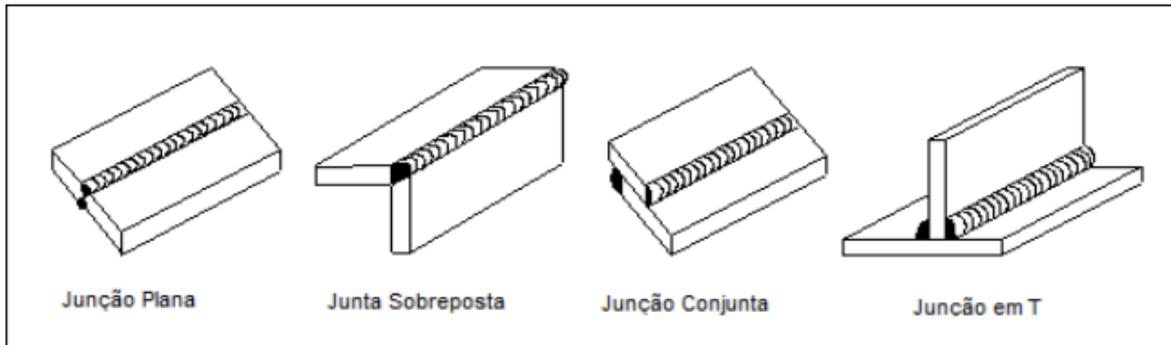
Tipos de junta na soldagem com eletrodo revestido
